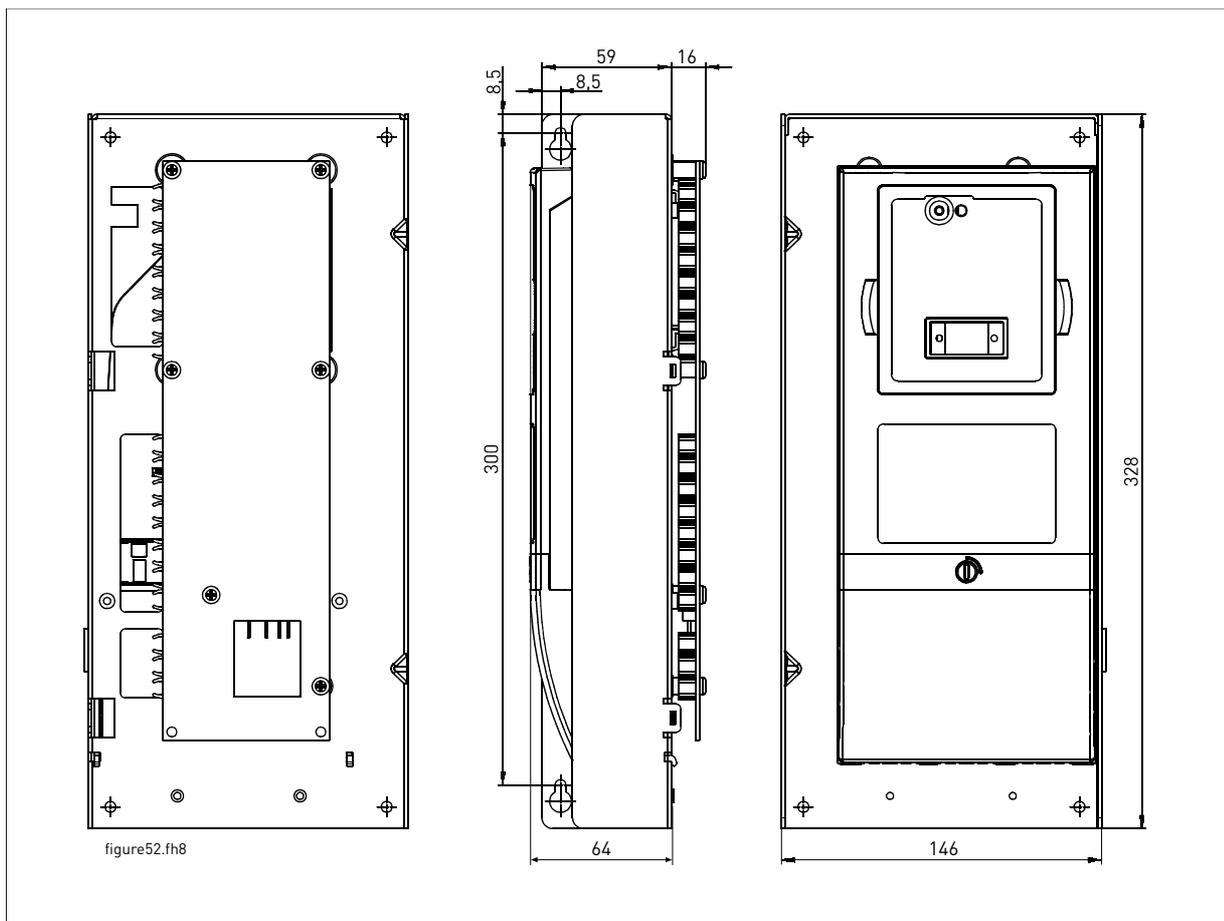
Dimensions de l'unité de commande (avec carte de couplage étoile connectée ; pour la taille FR12 ou FR14 uniquement)
